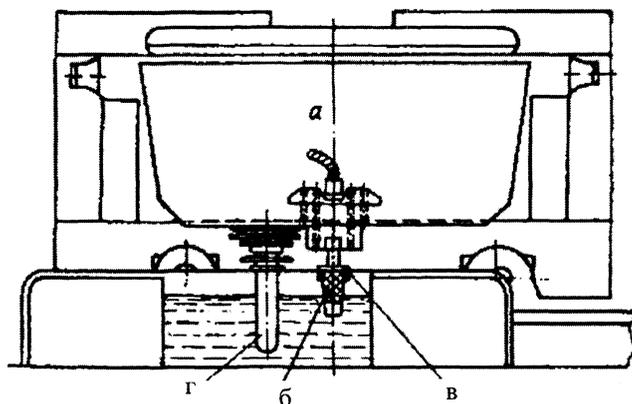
Схема установки для обработки стали вибрацией в кристаллизатор МНЛЗ: а – промежуточный ковш; б – виброинструмент; в – держатель виброинструмента; г – погружной стакан
